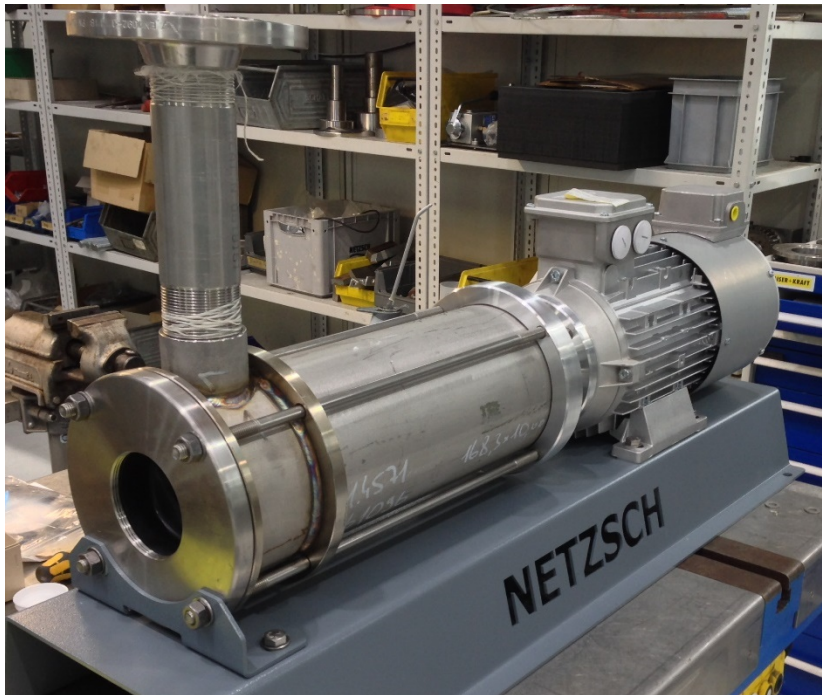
Prototyp einer neu entwickelte Wobbel-Pumpe mit standardisierter Anschlussgeometrie
